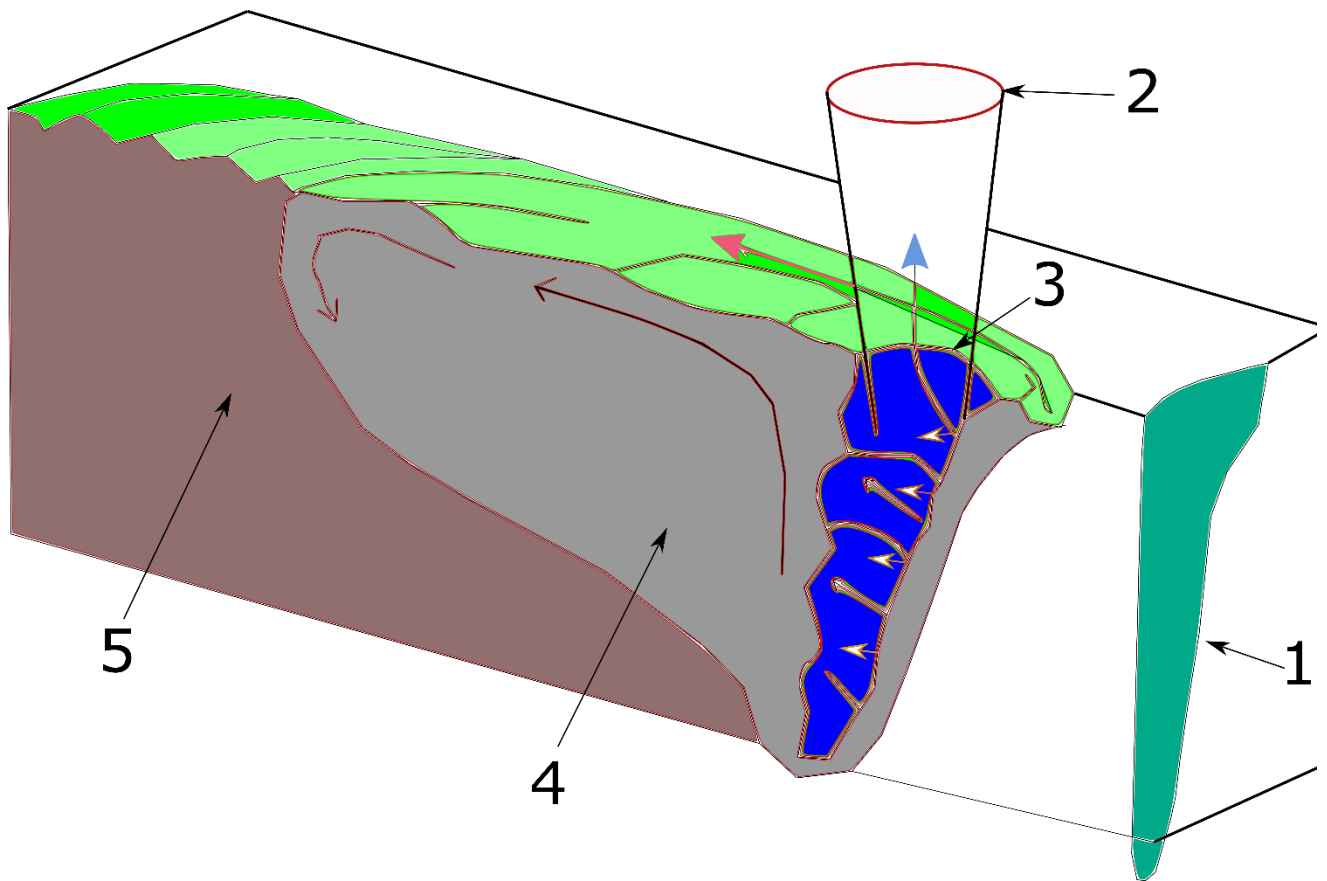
Схема лазерной сварки в режиме кинжального проплавления.
